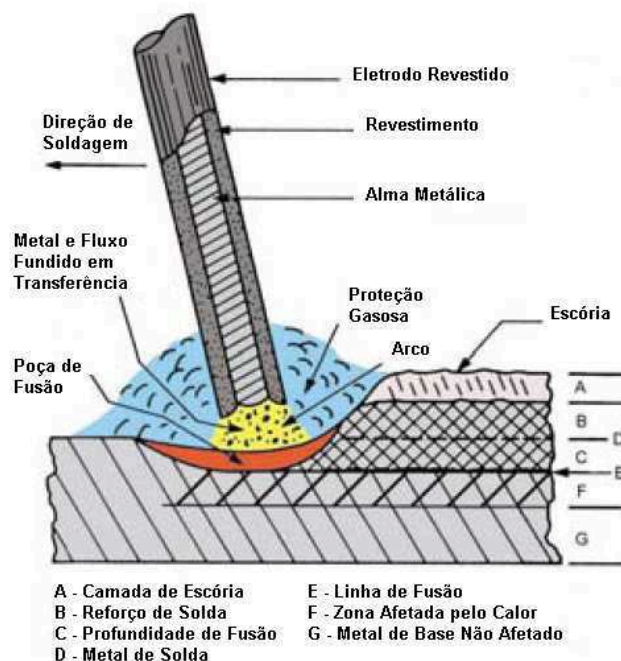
Esquema geral do processo de soldagem SMAW (adaptado de AWS HANDBOOK, 2004)
